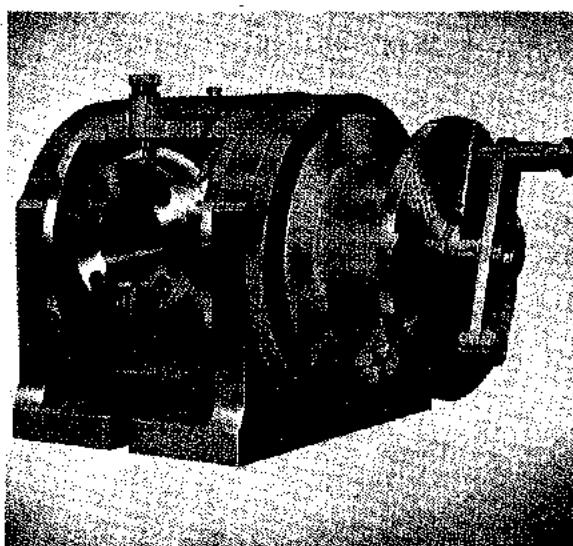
Cabezal divisor (Cincinnati Milling Machine Co.)
